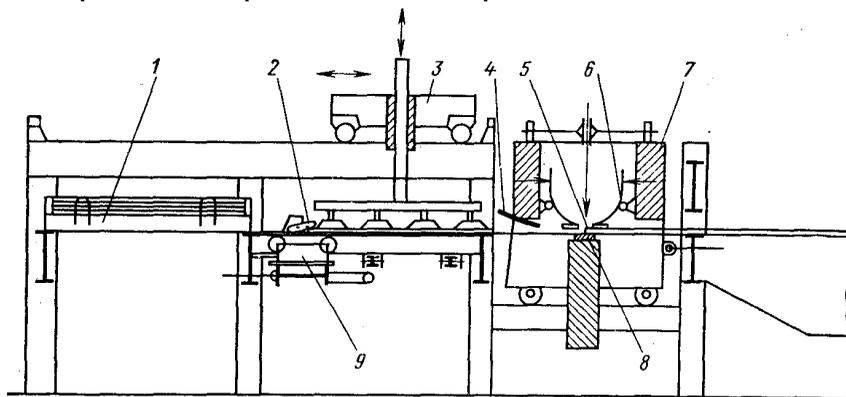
Схема расположения механизмов, обеспечивающих сборку секции и сварку поперечного шва
